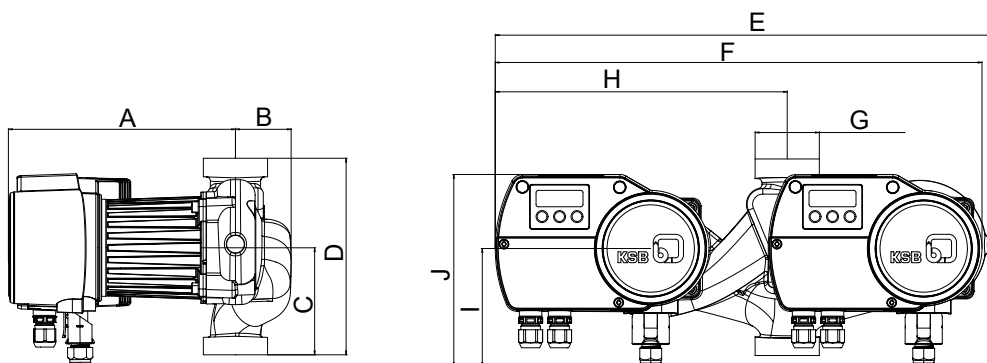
Pumpenaggregat mit Gewindeanschluss
